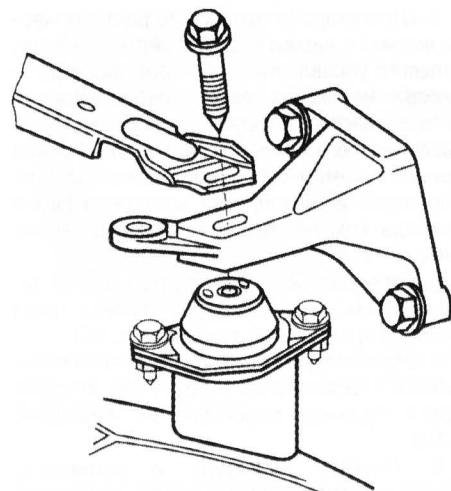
Элементы левой задней опоры и рычага подвески силового агрегата
